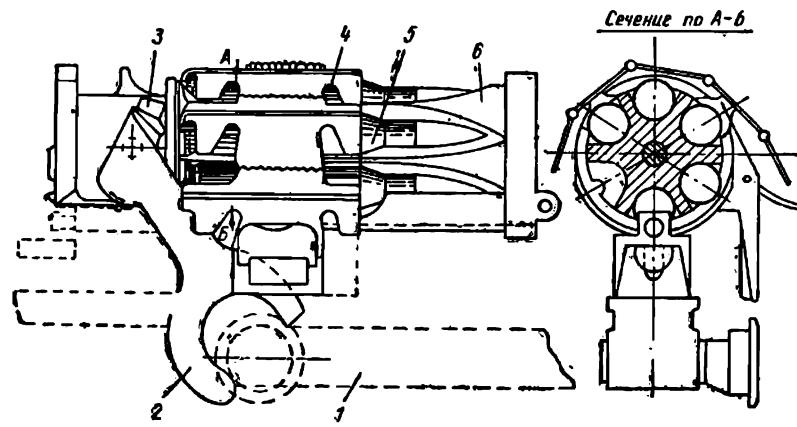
Конструктивная схема барабанного механизма подачи ленты:
